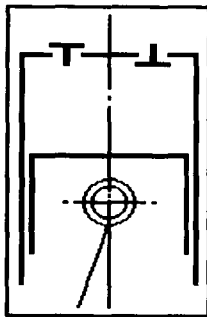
Pistón de un compresor de simple efecto.
